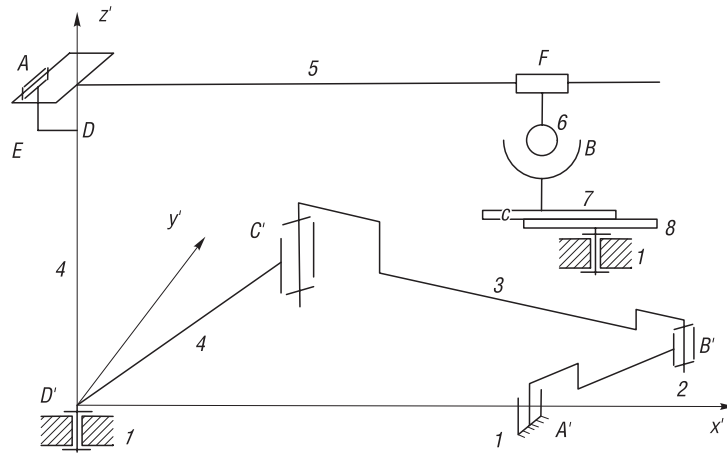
Кинематическая схема исполнительного механизма рычажного станка
